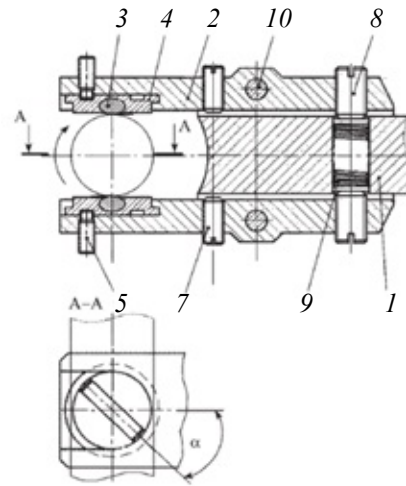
Устройство для упрочняющей поверхностной обработки цилиндрических деталей:
